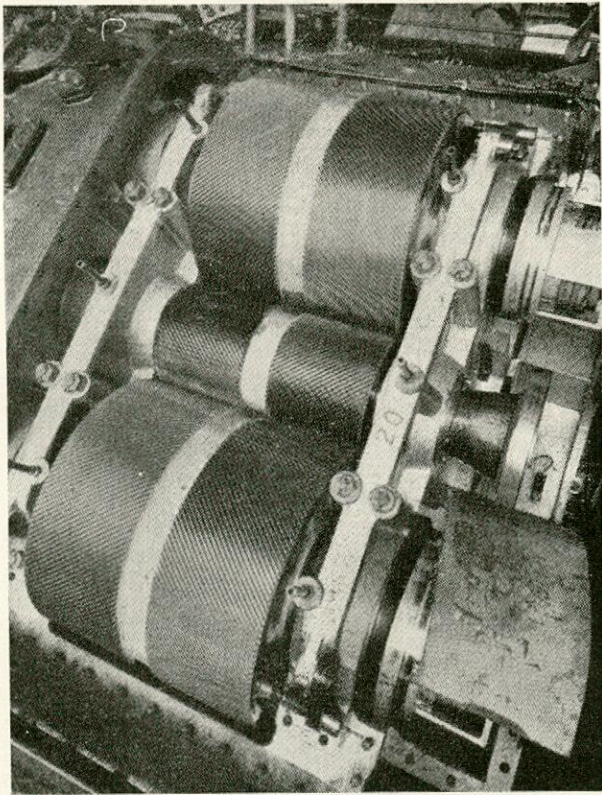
Destruyores "Daring". Engranaje principal, proyecto Pametrada. Vista del tren primario mirando a popa.
